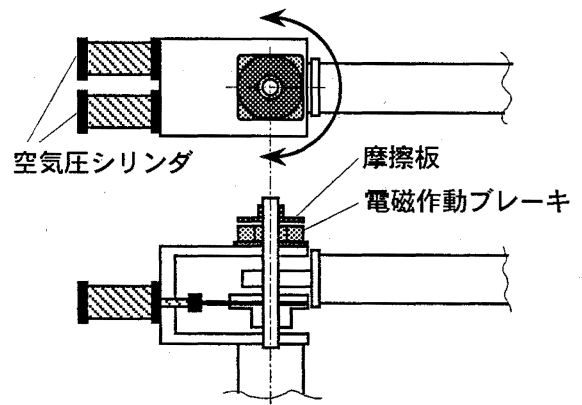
Construction of the shoulder joint. 肩関節部の構造
